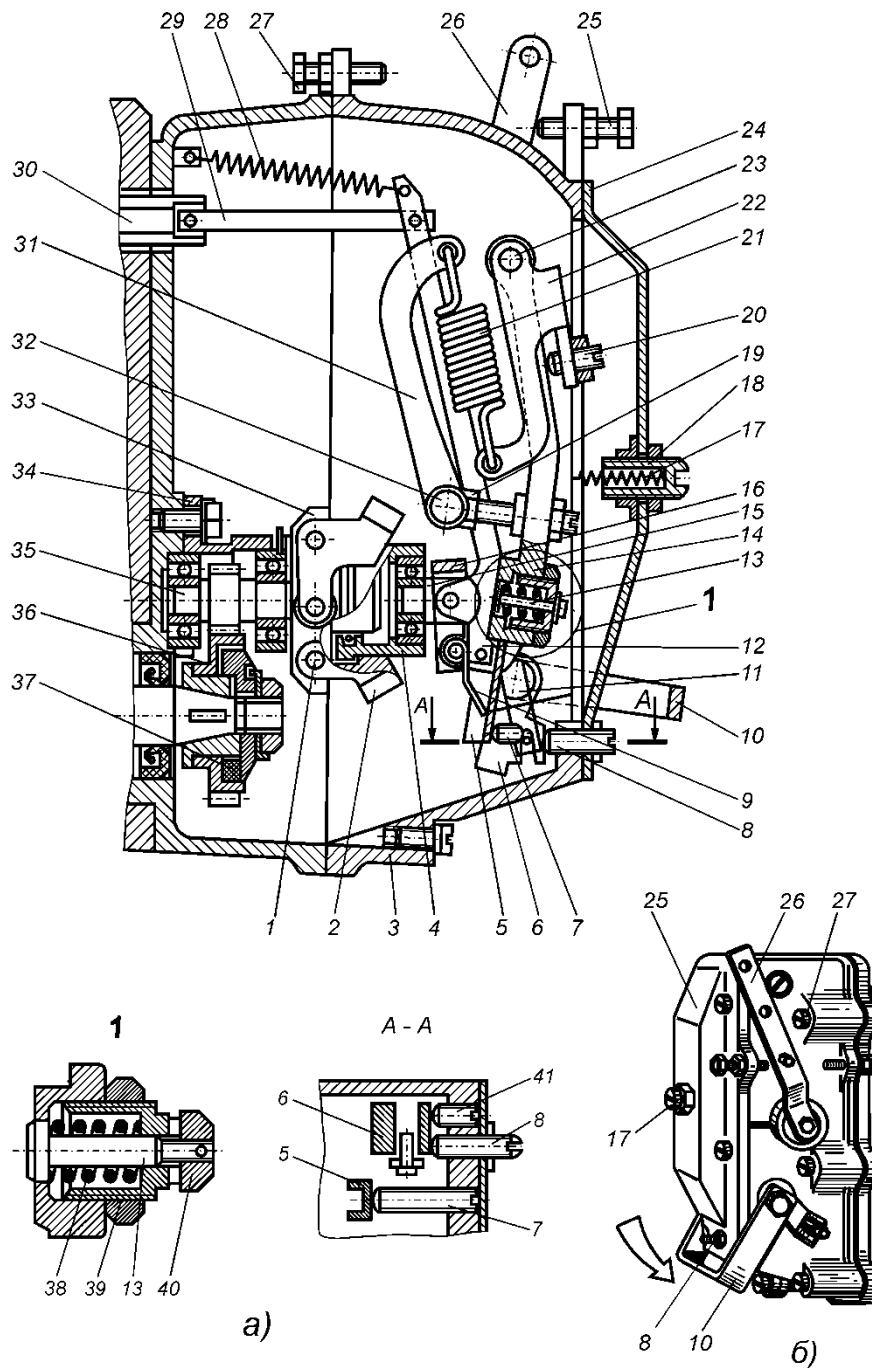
Регулятор ЯМЗ-240Б (а), детали крышки (б):
